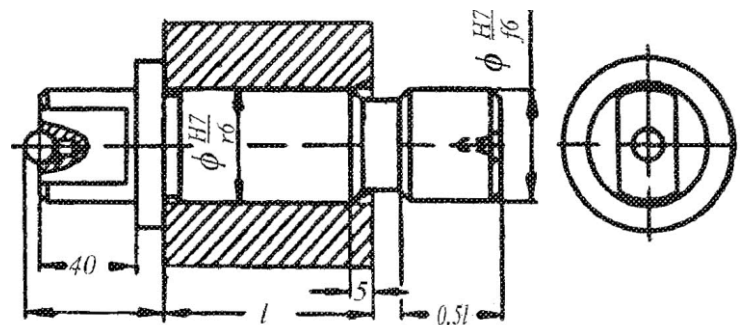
Установа заготовок на жорсткій оправці (посадка з зазором)
